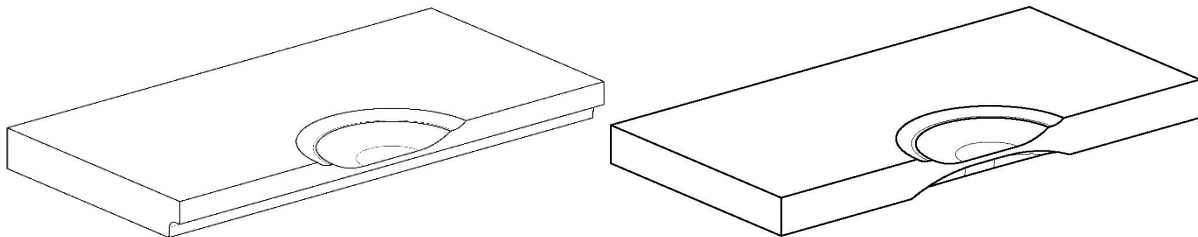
Schematische Zeichnung der Rohlingsgeometrie nach erfolgter Schweißnahtvorbereitung zur Kreuzprobenschweißung
